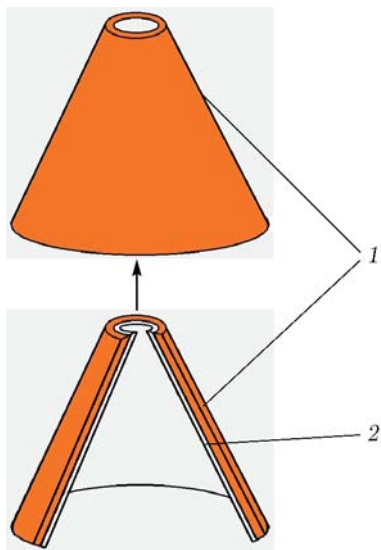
Схема сборки медь-медь-константановой облицовки:
